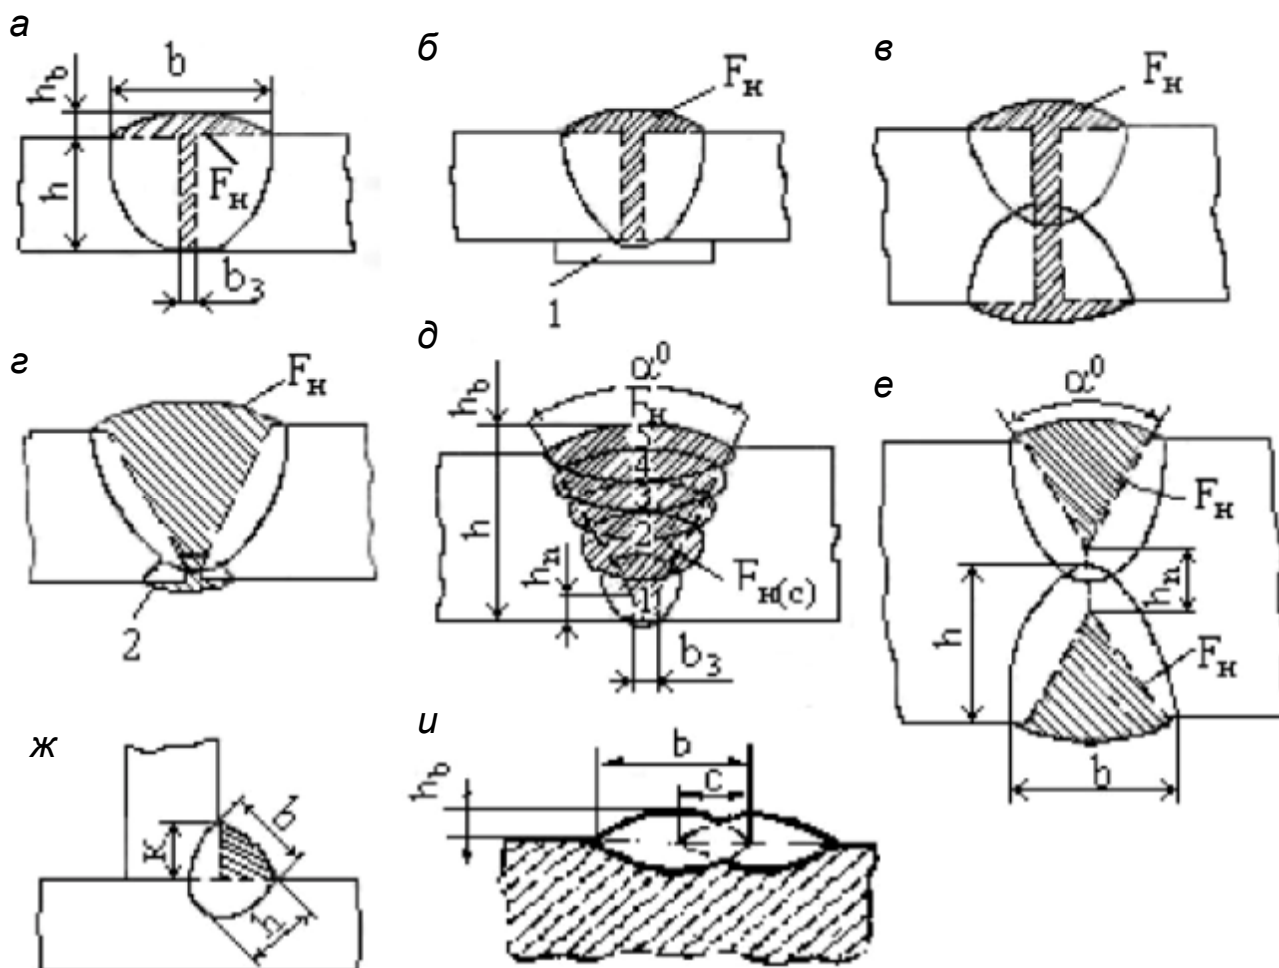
Размеры и форма разделки кромок и сварного шва: а – I-образная (без скоса кромок), односторонний стыковой шов; б – то же с металлической (остающейся) подкладкой 1; в – I-образная (без скоса кромок), двухсторонний стыковой шов; г – V-образная, стыковой шов с подваркой 2 корня шва; д – V-образная, многопроходной стыковой шов (цифры указывают номер прохода – слоя); е – X-образная, двухсторонний стыковой шов; ж – угловой шов (без скоса кромки вертикального элемента); и – расположение валиков при наплавке
